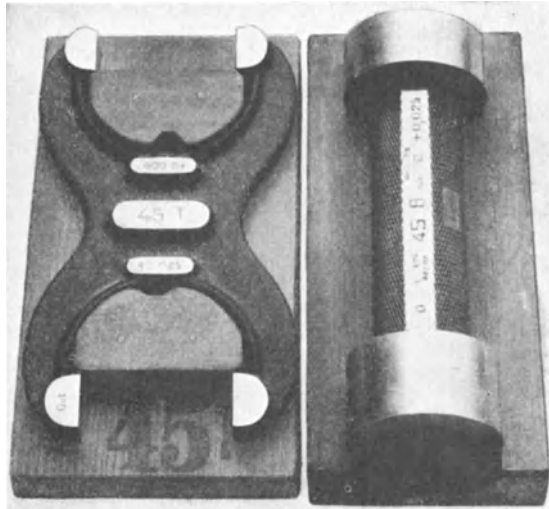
Meßwerkzeuge auf Holzbrettchen.
